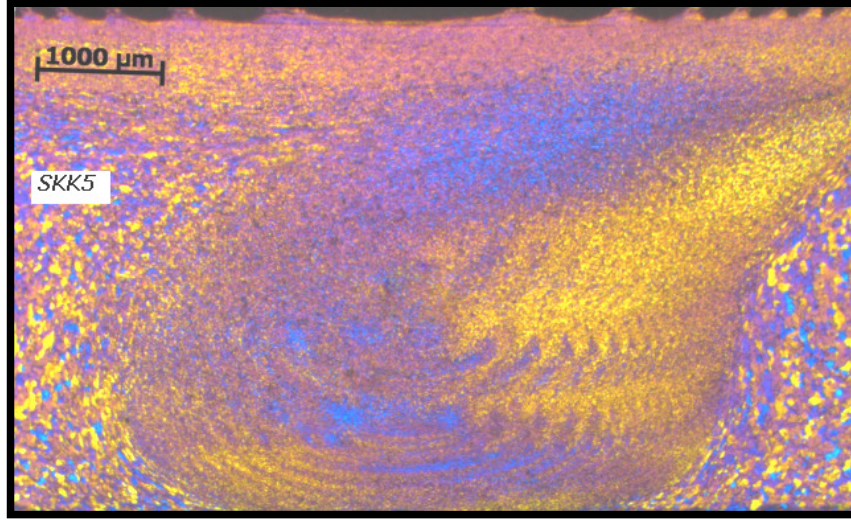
1600 dev/dak takım devrinde elde edilen kaynak metalinin makro yapısı.
